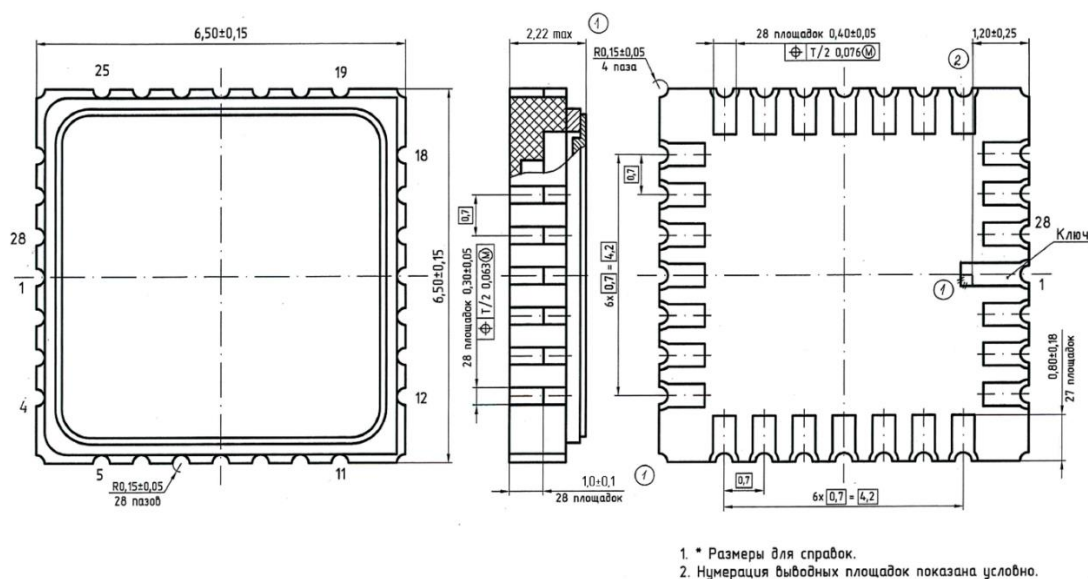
Габаритный чертеж корпуса 5123.28-1.01 (размеры в мм)
